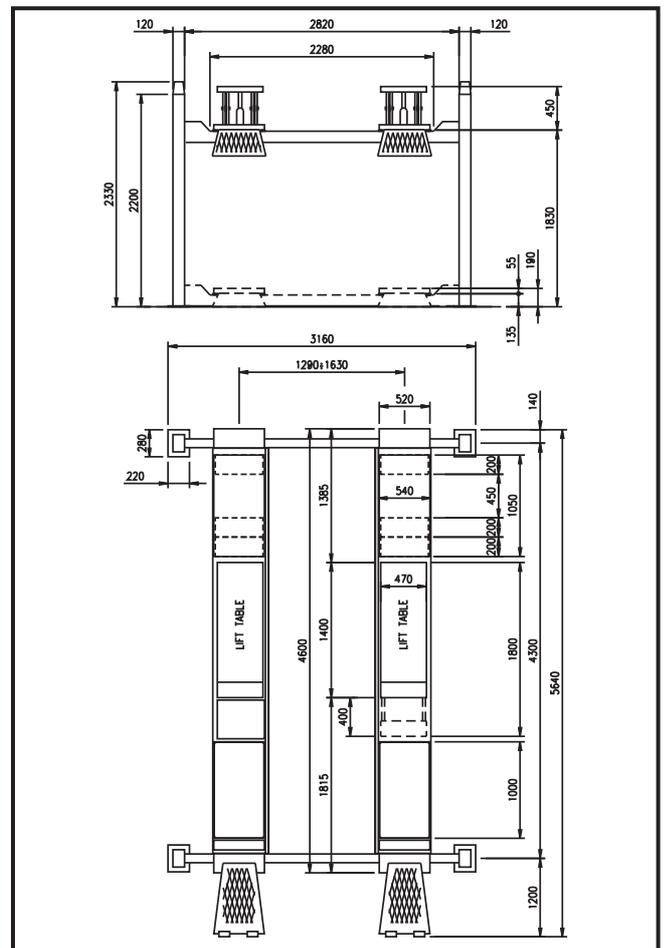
Dimensioni ed ingombri con kit assetto ruote
